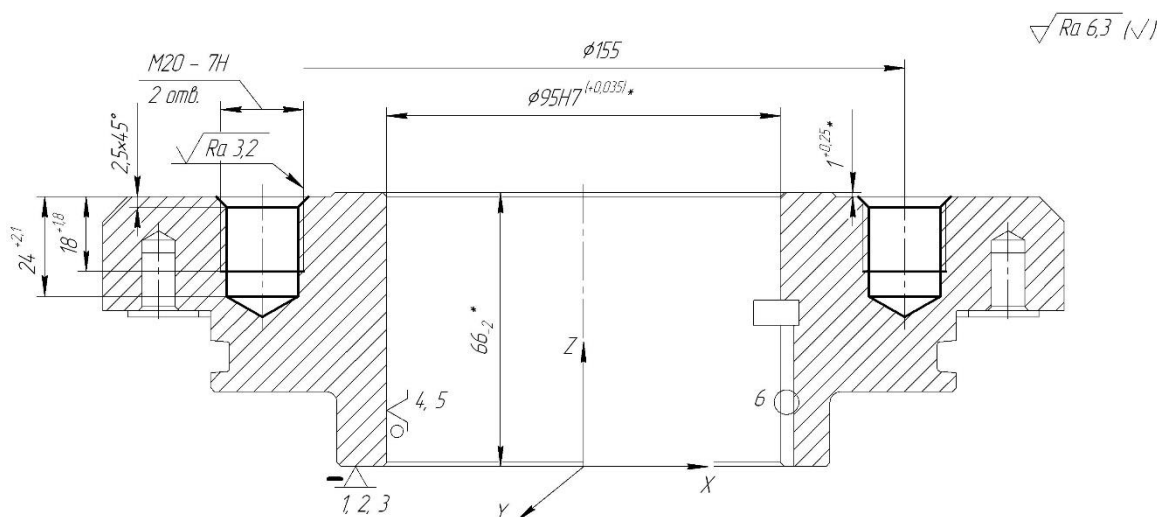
Схема базування і закріплення заготовки на операції комплексній на обробному центрі з ЧПК, установ Б
